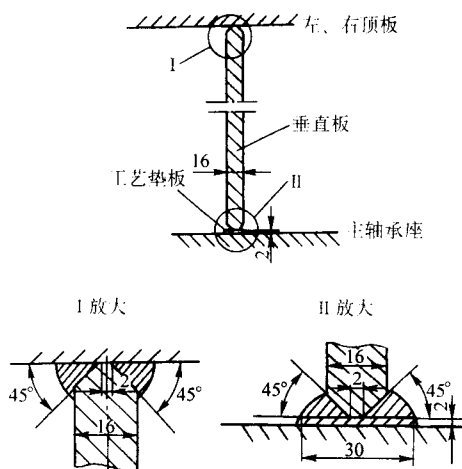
垂直板与主轴承座及顶板的焊接接头
